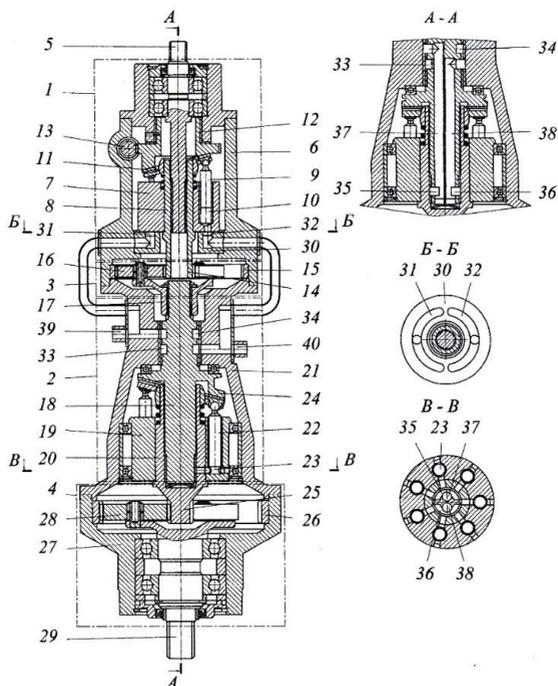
Конструктивная схема ОГП с внутренним разветвлением потока мощности
